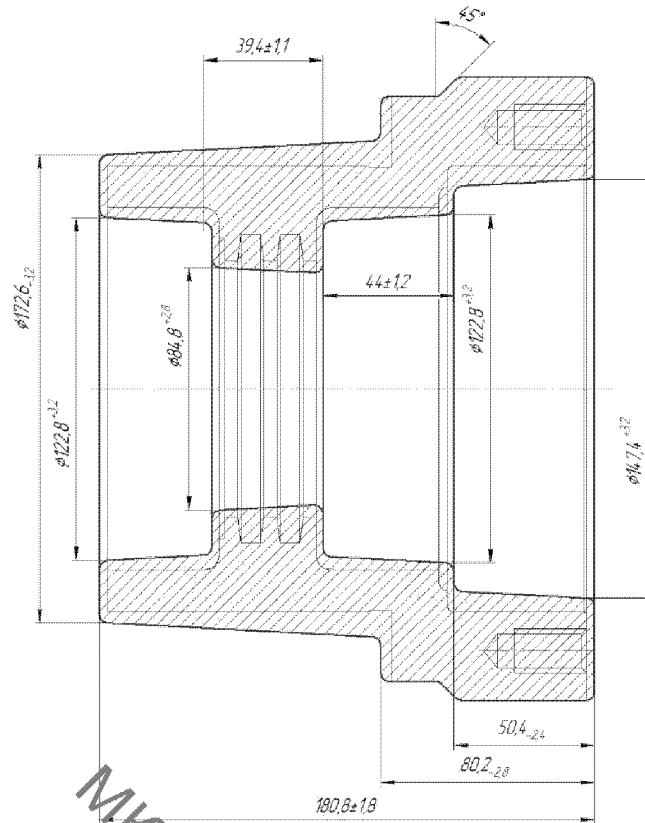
Ескіз заготовки в піщано-глинисті форми
